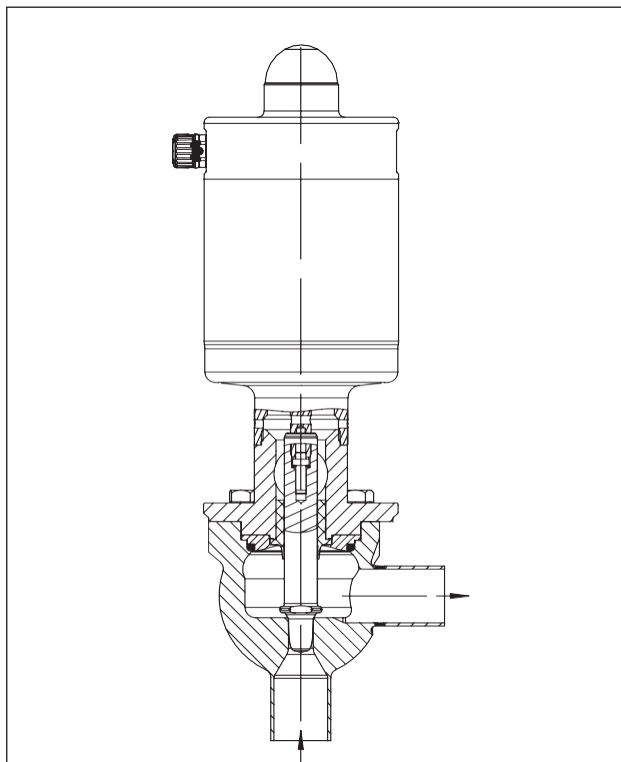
Регулирующий клапан Тип 3347/3379 с концами под приварку. Цельное исполнение с верхней частью на болтах
